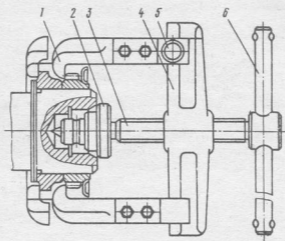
Снятие шестерни и заднего противовеса коленчатого вала съемником И-801.01.000:
